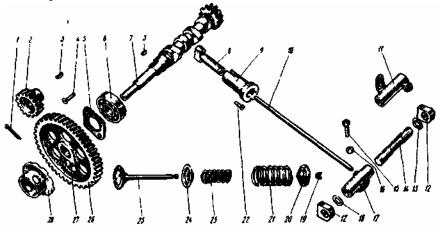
Детали механизма газораспределения двигателя мотоциклов "Урал": 1 - шплинт; 2 - зубчатое колесо генератора; 3 - шпонка; 4, 22 - винты; 5 - фланец распределительного вала; 6 - подшипник; 7 - распределительный вал с зубчатым колесом смазочного насоса; 8 - толкатель, 9 - направляющие; 10 - штанга; 11 - коромысло; 12 - кронштейн оси коромысла; 13 - пружинная шайба; 14 - ось коромысла; 15 - регулировочный болт; 16 - контргайка, 17 - левое коромысло; 18 - упорная шайба; 19 - сухарь; 20, 24 - верхняя и нижняя тарелки клапанной пружины; 21 - наружная пружина клапана; 23 - внутренняя пружина клапана; 25 - клапан; 26 - зубчатое колесо распределительного вала; 27 - поводок сапуна; 28 - сапун
